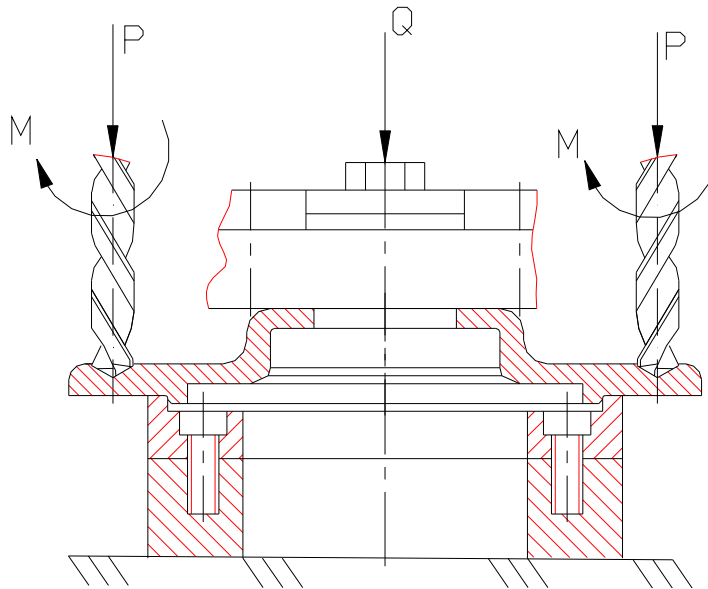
Розрахункова схема сил при свердлінні у кондукторі
